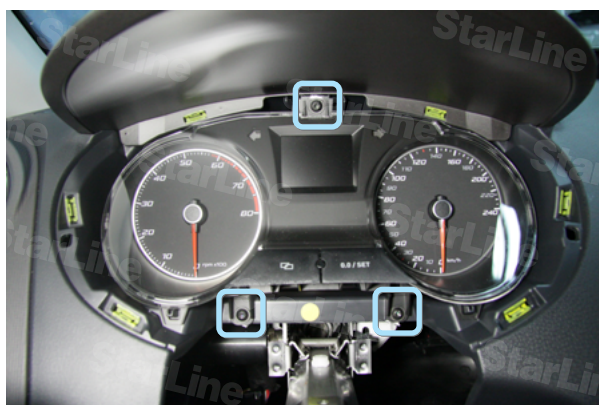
Накладка щитка приборов снята, саморезы крепления щитка
